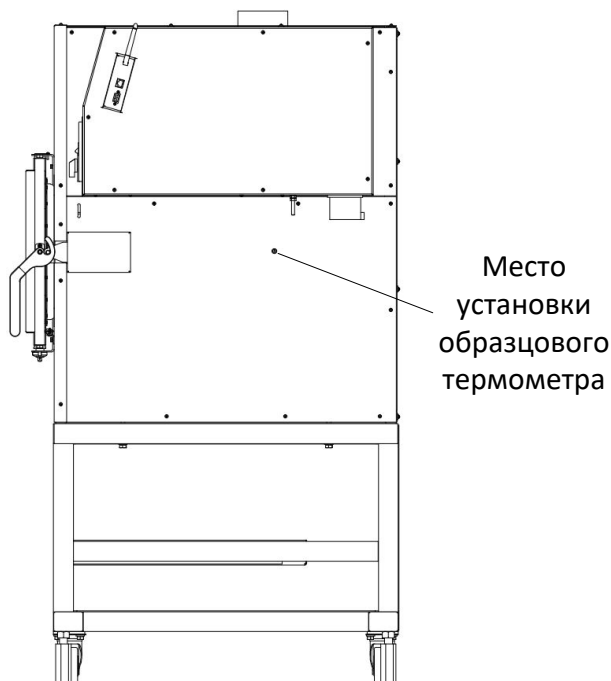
Место установки образцового термометра (вид печи сбоку)
